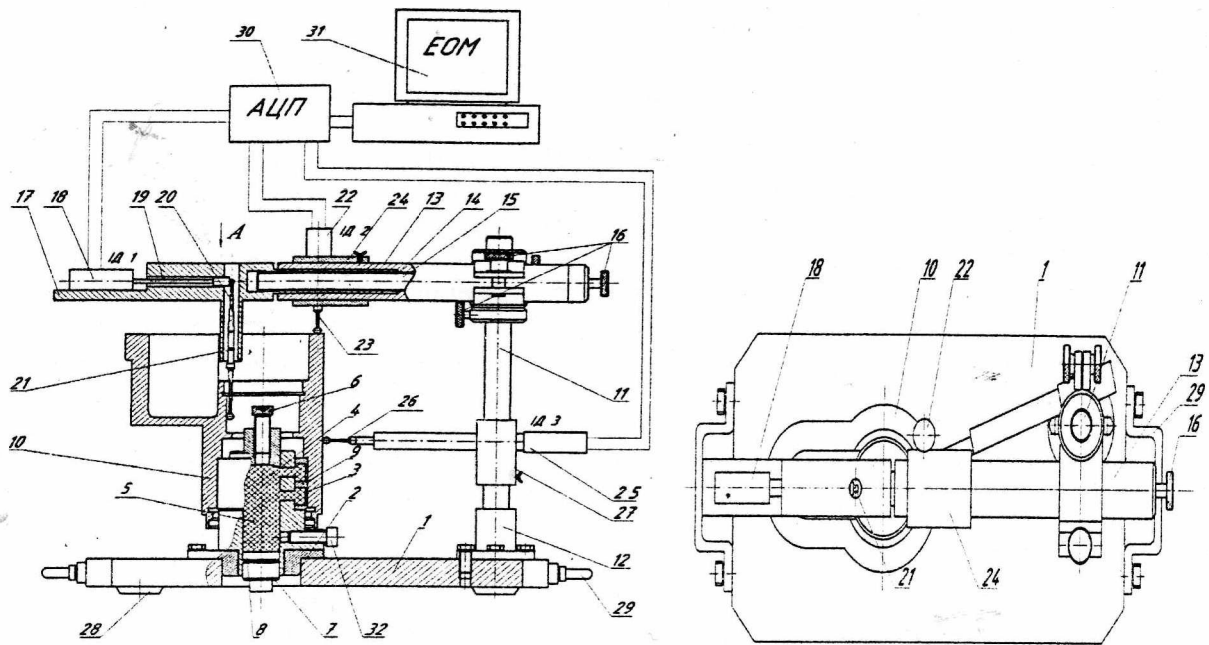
Пристрій для заміру параметрів корпусних деталей
